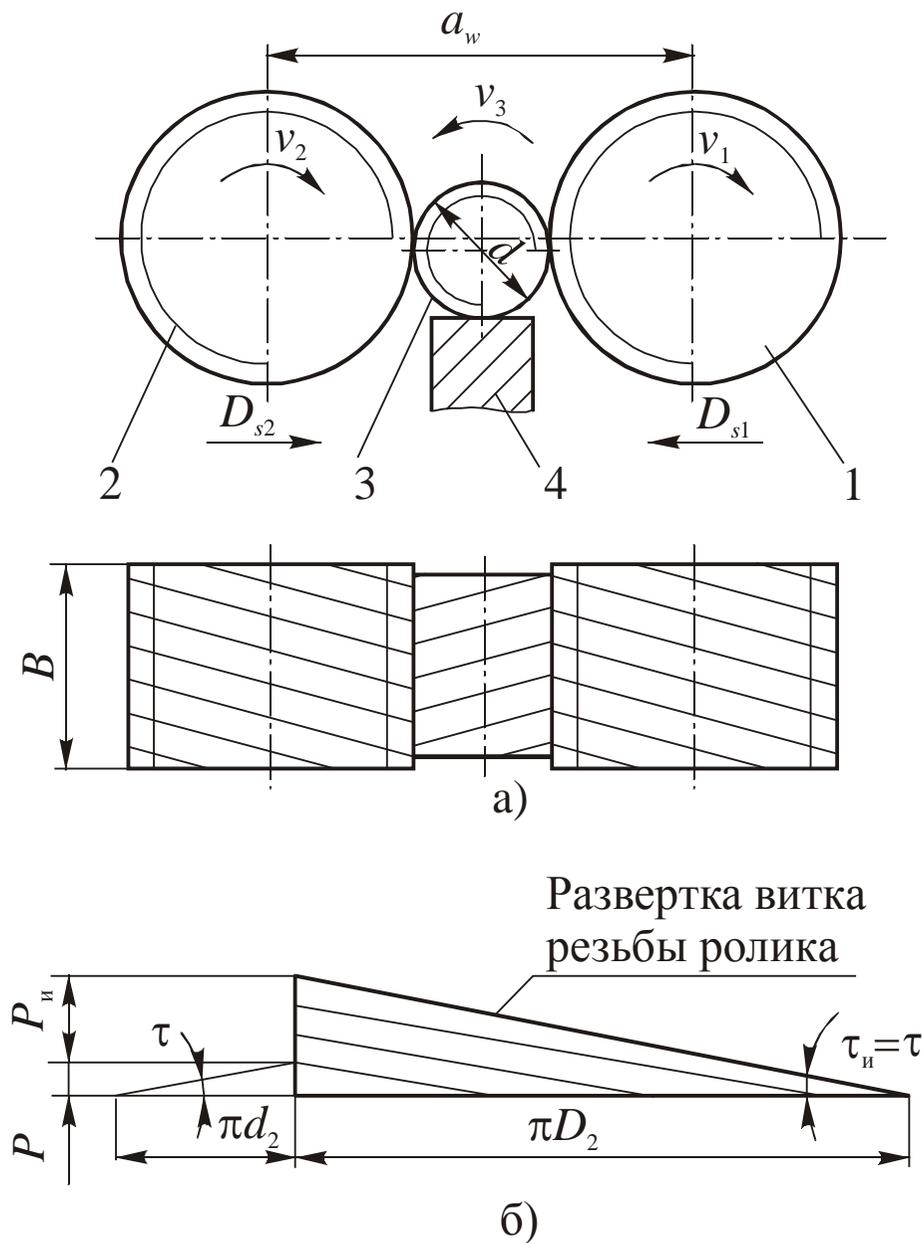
Накатывание резьбы круглыми плашками с радиальной подачей: а – схема накатывания; б – развертка витка резьбы ролика
